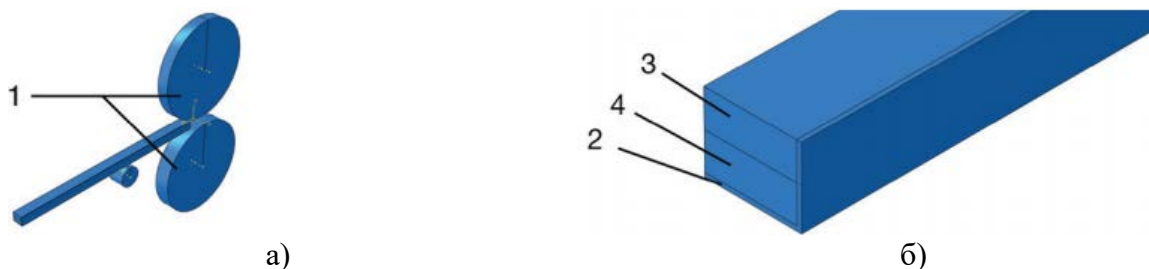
Конечно-элементная модель процесса прокатки двухслойной порошковой ленты а – расчётная схема; б – заготовка:
